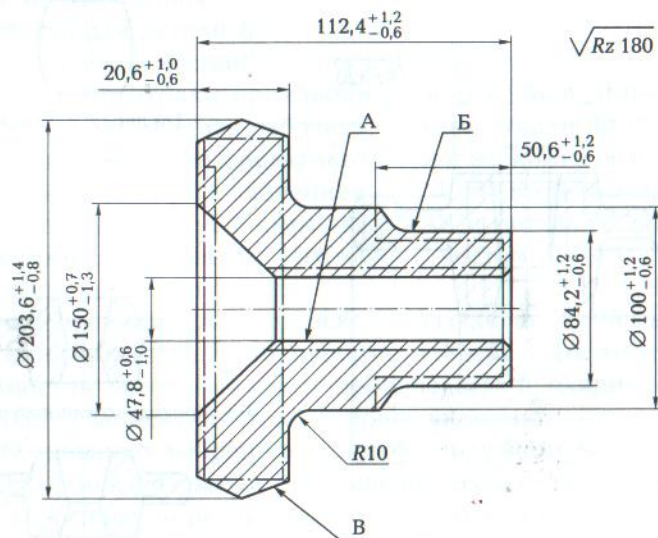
Пример оформления рабочего чертежа штампованной заготовки
